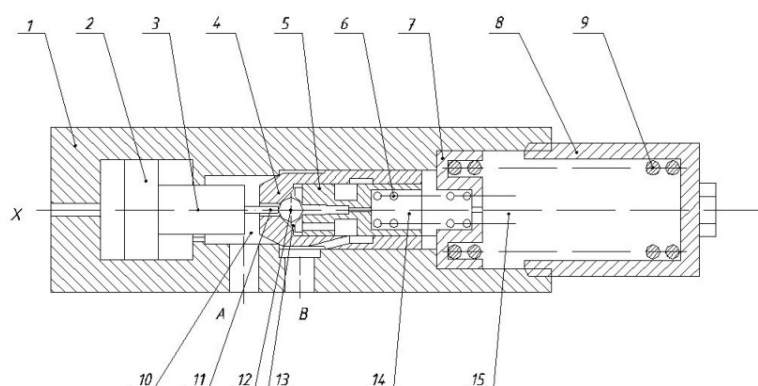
Предлагаемый тормозной клапан: 1 – корпус; 2 – поршень; 3 – направляющая поршня; 4 – запорно-регулирующий элемент; 5 – золотник; 6 – пружина; 7 – шайба; 8 – седло; 9 – пружина; 10 – полость; 11 – толкатель; 12 – шариковый клапан; 13, 14, 15 – полости
